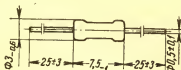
Габаритный чертеж диодов 2Д503А и 2Д503Б.
